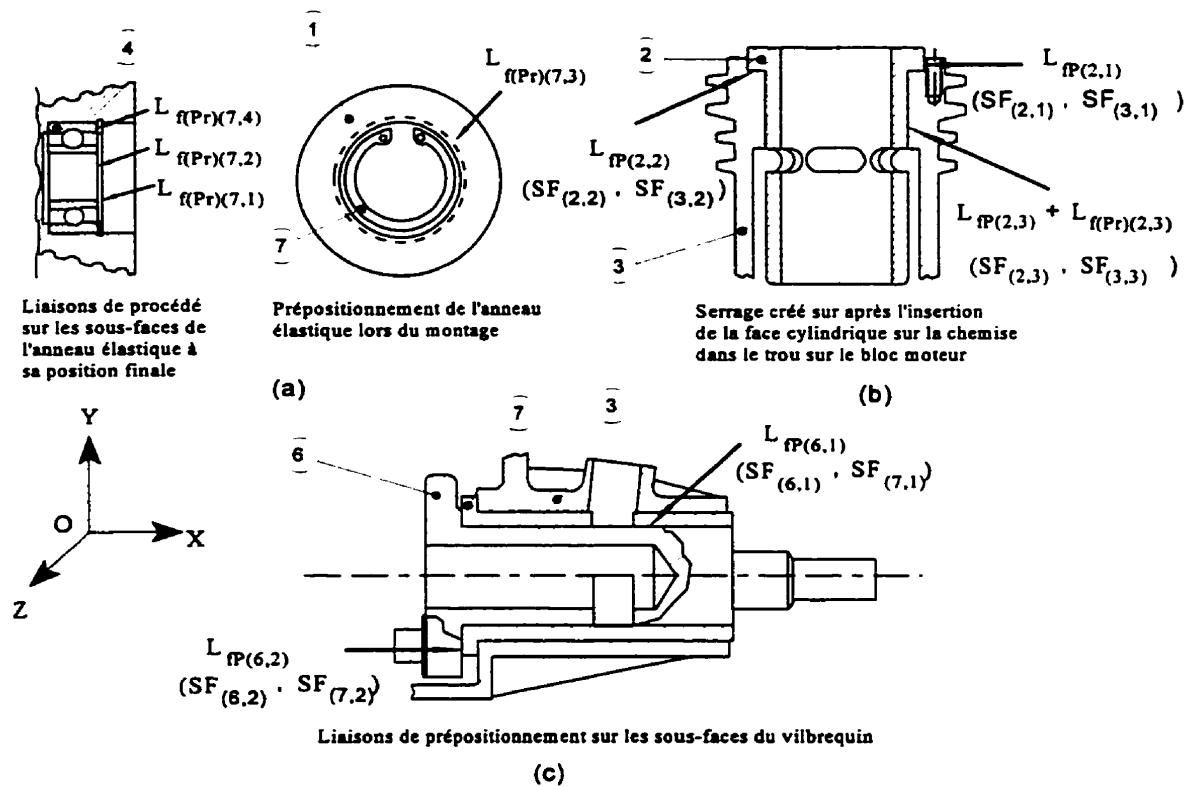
Exemples sur la méthode d'assemblage des pièces
